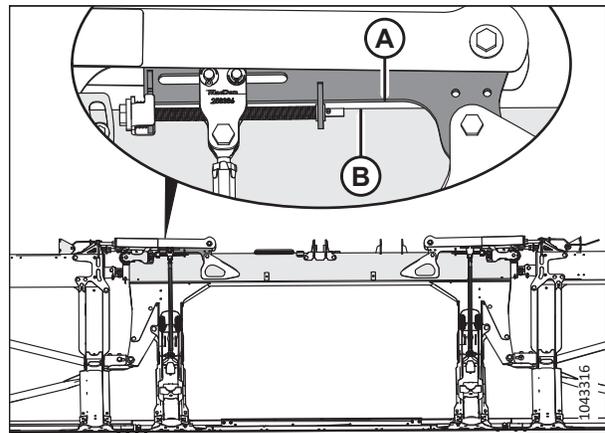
Parallélisme du levier coudé et du tube arrière
